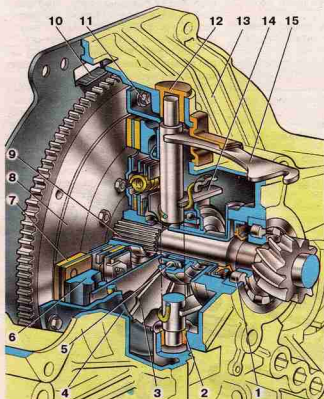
Сцепление в сборе: 1 – роликовый подшипник первичного вала; 2 – опорная втулка вилки выключения сцепления; 3 – нажимная пружина; 4 – кожух сцепления; 5 – подшипник выключения сцепления; 6 – нажимной диск; 7 – ведомый диск; 8 – маховик; 9 – первичный вал коробки передач; 10 – шкала; 11 – болт крепления сцепления к маховику; 12 – втулка вилки выключения сцепления; 13 – картер сцепления; 14 – вилка выключения сцепления; 15 – рычаг вилки выключения сцепления
